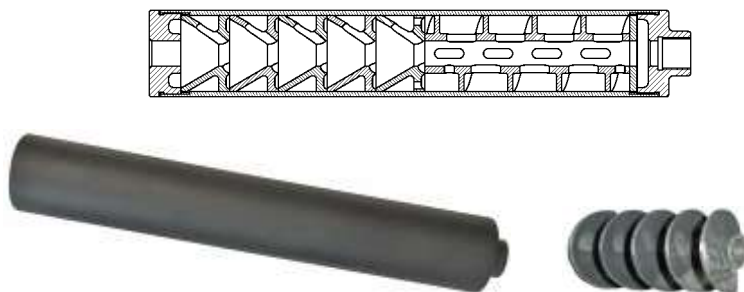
Конструктивная схема и внешний вид ПСУЗВ-15АТ.18-9,0
